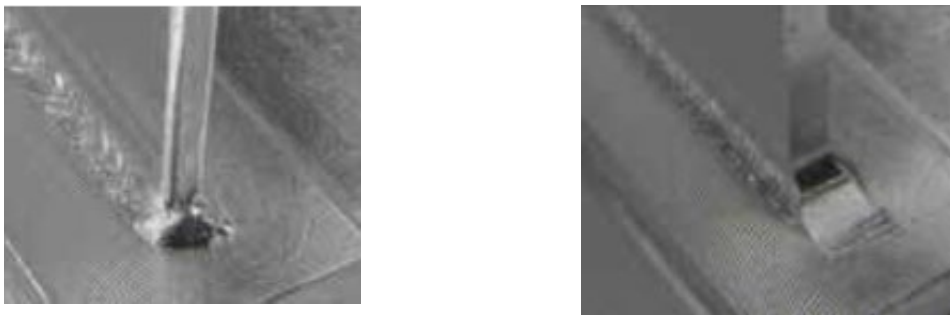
Локальное фрезерование начала сварного шва; слева без фрезеровки; справа: после локальной фрезеровки
